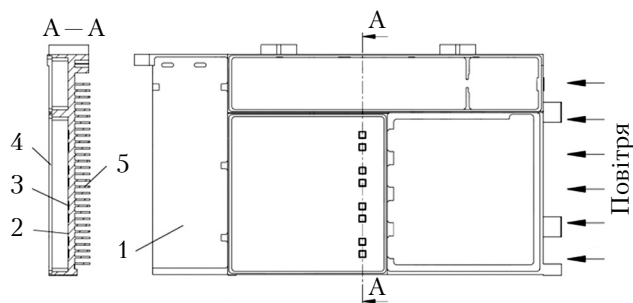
Конструктивна схема корпусу-радіатора: 1 — несуча основа; 2 — монтажна сторона основи; 3 — місце установки тепловиділяючого елемента; 4 — місце для установки кришки; 5 — ребро охолодження
